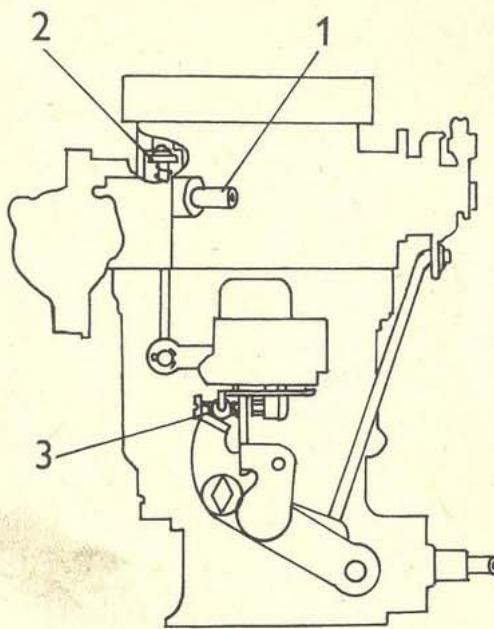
Seřizování plováku karburátoru K - 131 A (K - 131)
